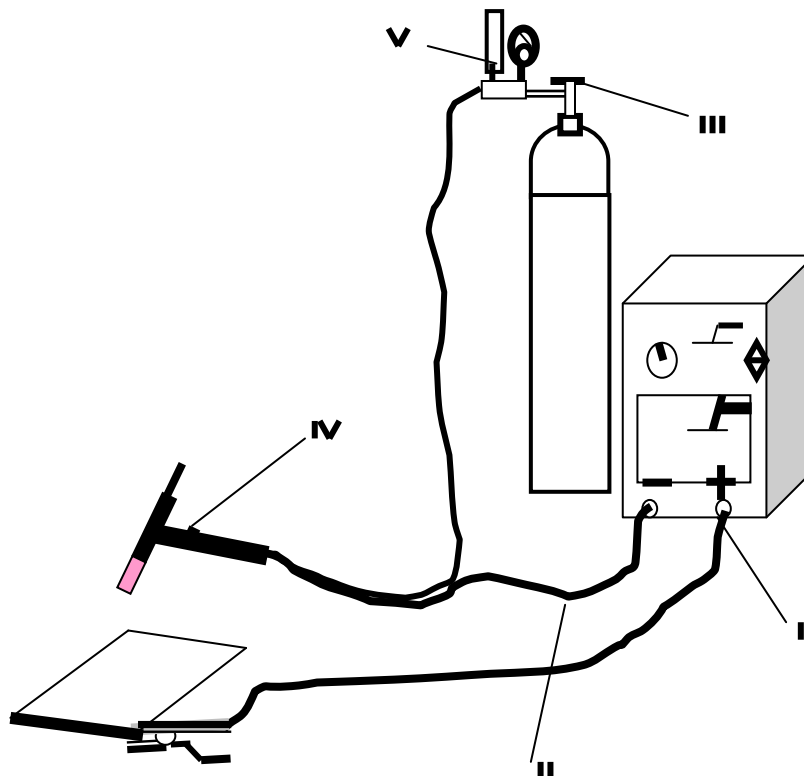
Conexiones principales de una instalación convencional de soldadura GTAW. I- Conexión a la pieza; II- Conexión a la antorcha; III- Conexión del gas protector ;IV- Control del flujo de salida de gas; V- Flujómetro.
